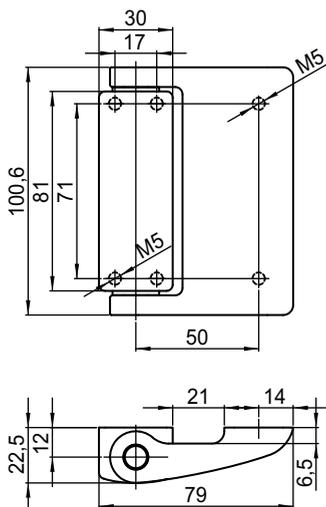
Dimensions de la charnière supplémentaire AC-H-S410 en mm
